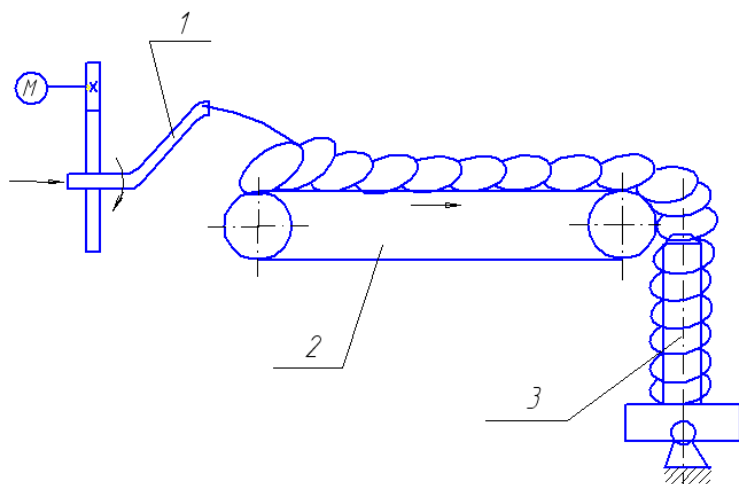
Схема укладки витков на установках двухстадийного охлаждения:
